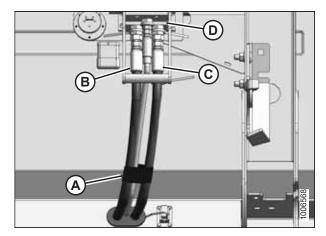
Multicoupleur à l'arrière de la plateforme
